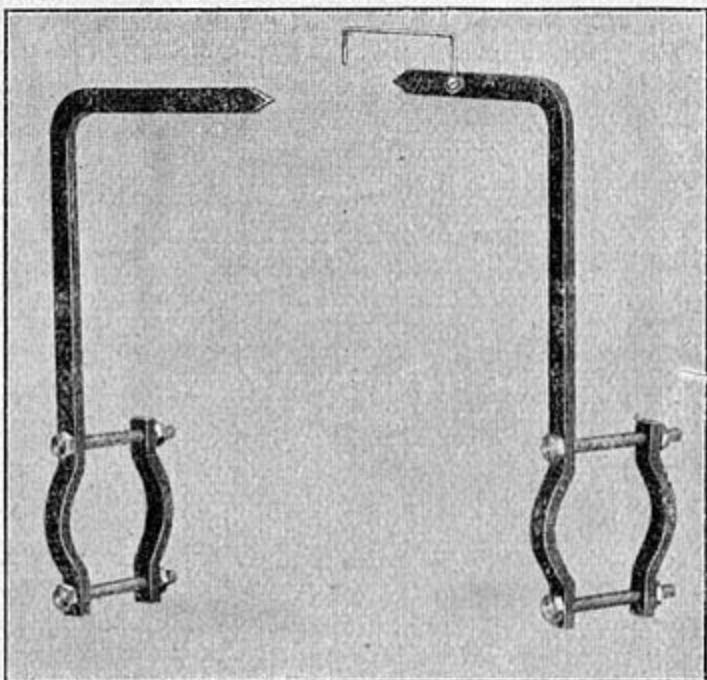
Werkzeug zum Ausrichten K 1449 direkt gekuppelter Maschinen.
